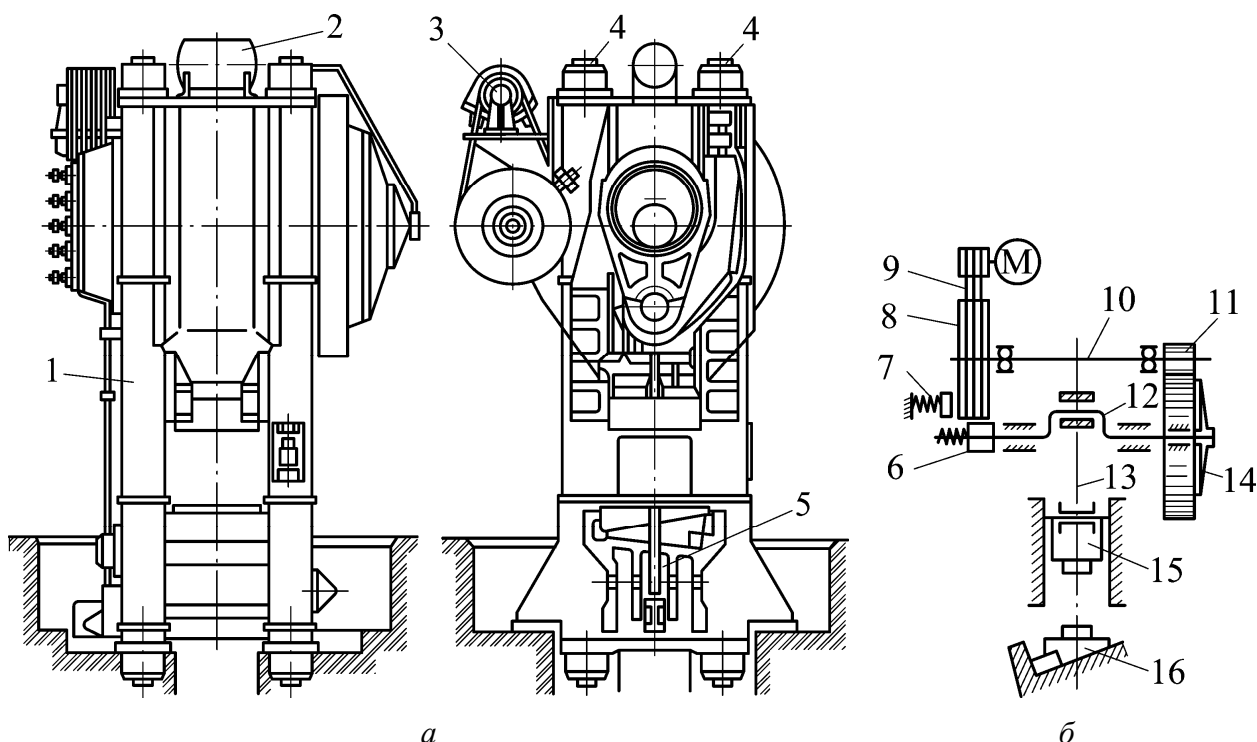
Общий вид (а) и кинематическая схема (б) КГШП: 1 – станина; 2 – ресивер; 3 – электродвигатель; 4 – стяжные болты; 5 – нижний выталкиватель; 6 – тормоз; 7 – тормоз маховика; 8 – маховик; 9 – клиноременная передача; 10 – промежуточный вал; 11 – зубчатая передача; 12 – главный кривошипный вал; 13 – шатун; 14 – пневматическая фрикционная муфта; 15 – ползун; 16 – стол с двуклиновым устройством
